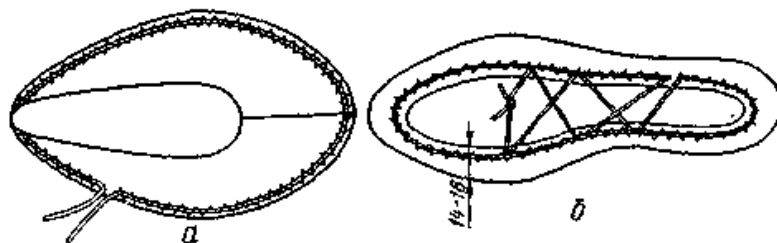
Схемы пристрачивания шнура к заготовке верха (а) и шнуровая затяжка (б)
